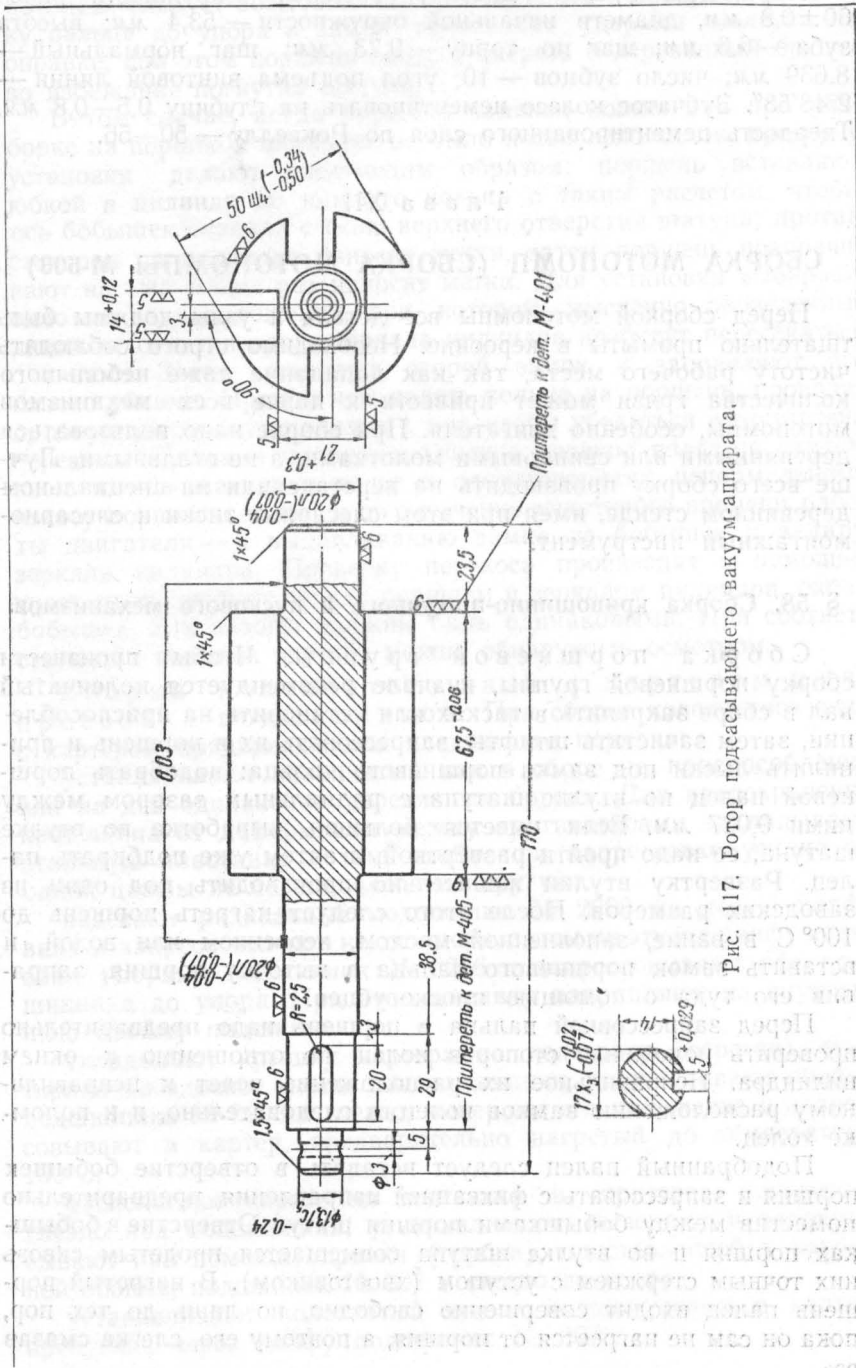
Ротор подсасывающего вакуум-аппарата.
